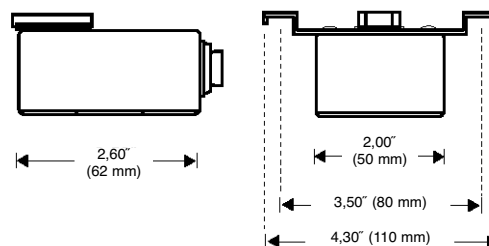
Les dimensions de la sonde de température TE-704 B sont exprimées en pouces et en millimètres (mm).
